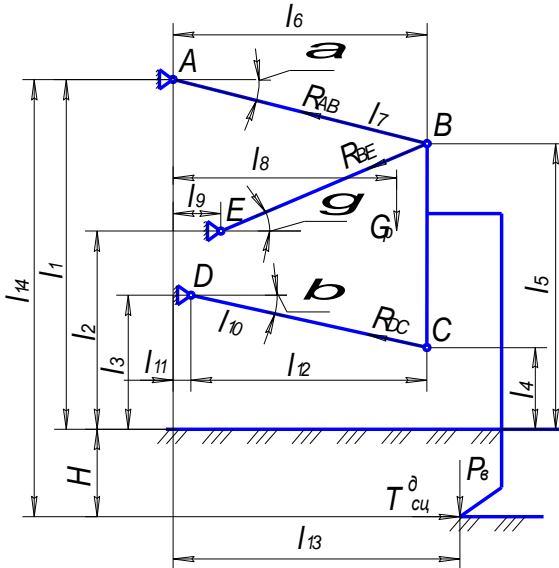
Розрахункова схема для визначення зусиль в стержнях при виглибленні зуба розпушувача.
